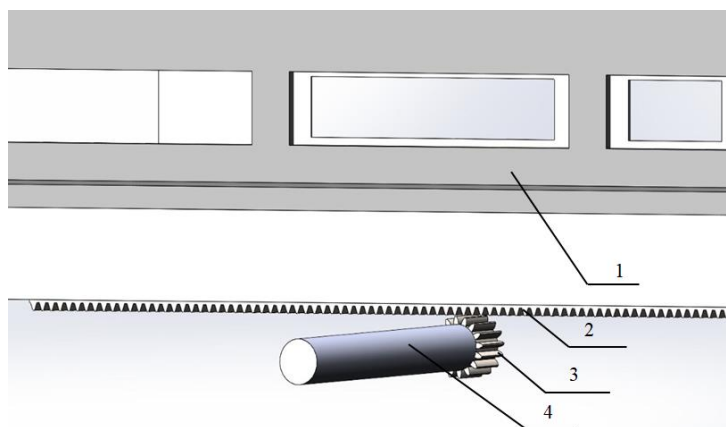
Модель принципа преобразования вращательного движения от вала в линейное поступательное рейки:
